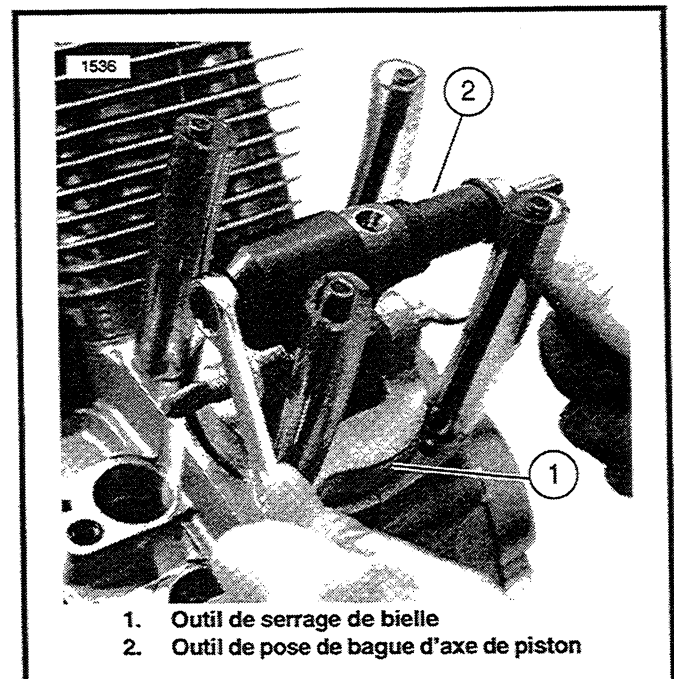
Installation d'une nouvelle bague d'axe de piston
